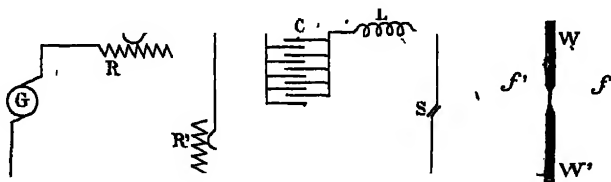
Soudure électrothermique des fils d'aluminium dispositif de l'installation.
